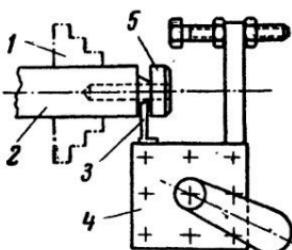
Применение подвижного упора при изгото- лении заготовок для гаек.
